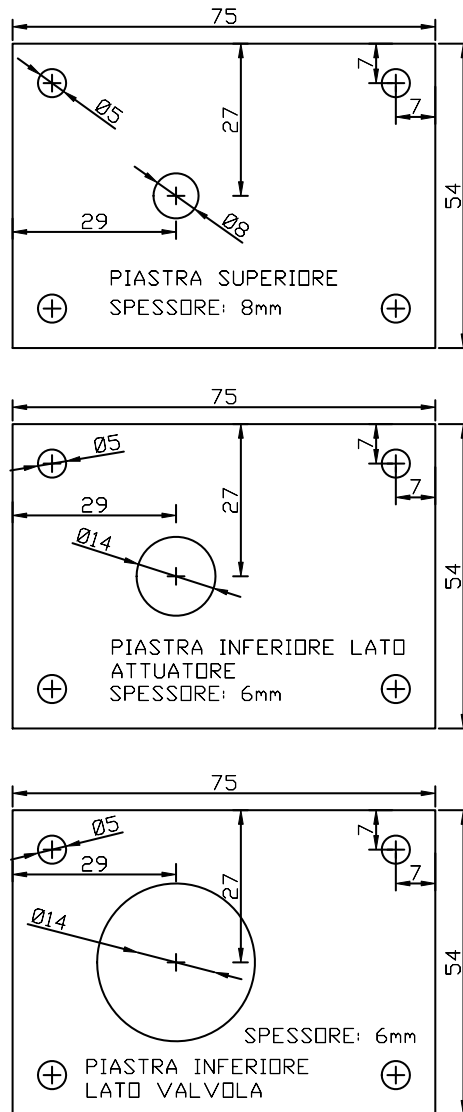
Disegno CAD della struttura di accoppiamento motoriduttore-valvola
